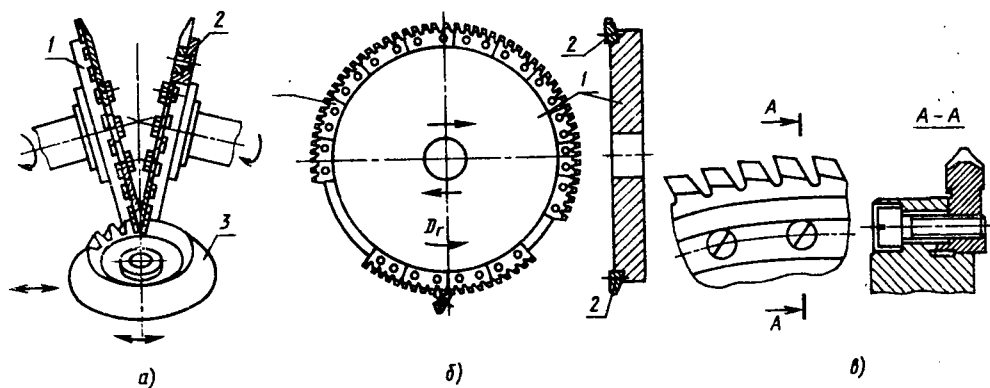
Фрезы и круговая протяжка для нарезания прямозубого конического колеса
